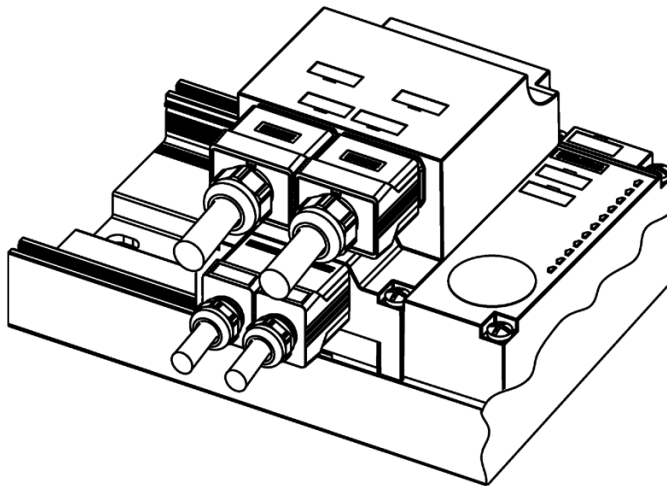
Push-Pull-Anschlussstecker anschließen
